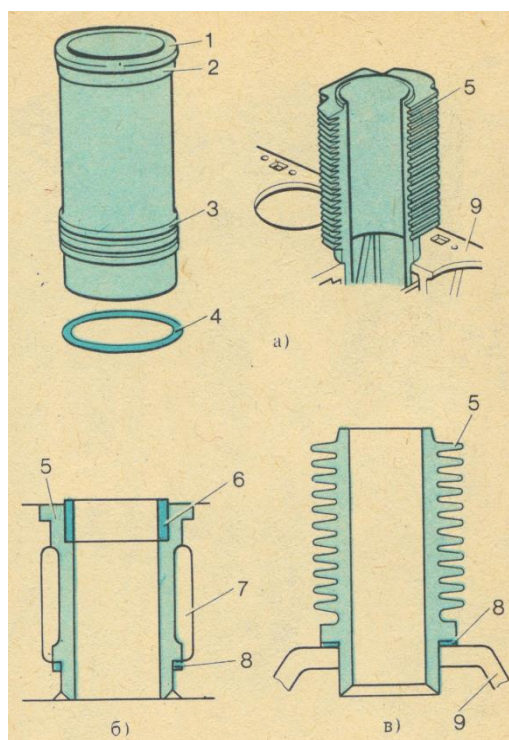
Конструкции цилиндров: а - "мокрая" гильза цилиндра, б - схема установки гильзы двигателя, в - цилиндр с воздушным охлаждением, 1 - буртик, 2 - верхний пояс, 3 - нижний пояс, 4 - резиновое уплотнительное кольцо, 5 - гильза цилиндра, 6 - вставка, 7 - водяная рубашка, 8 - уплотнительная прокладка, 9 - картер
